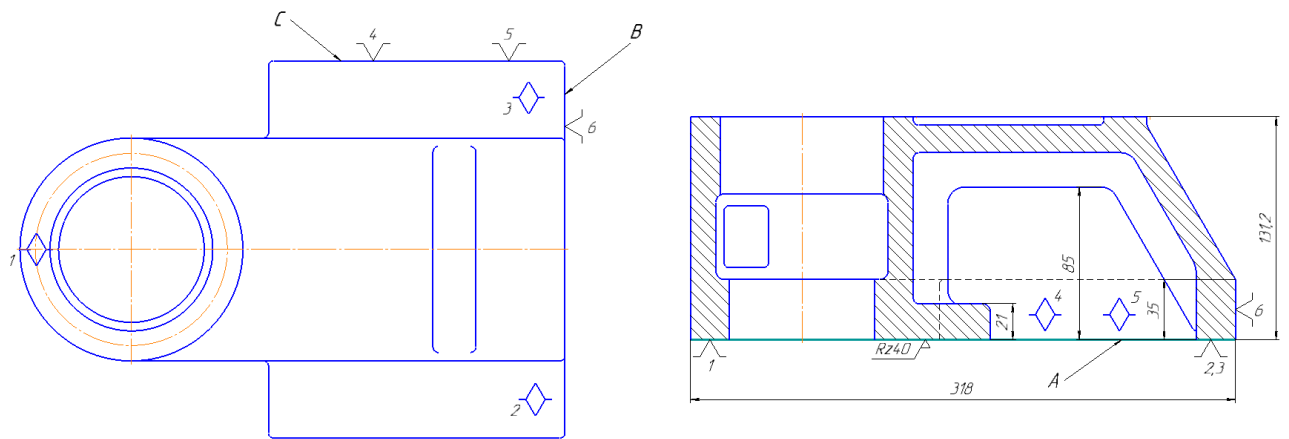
Схема базування та закріплення заготовки на операції 020 фрезерна
